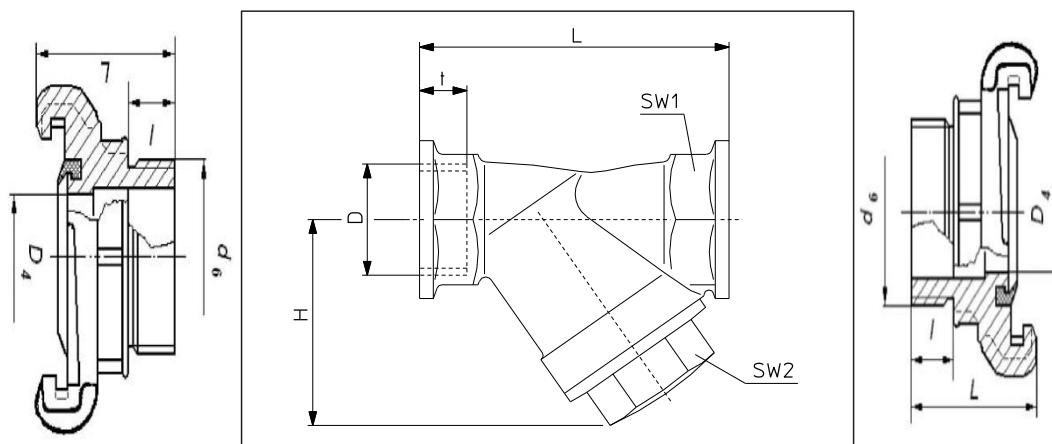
Схема монтажа фильтра с цапковыми соединительными головками ГЦ диаметром 80 мм
